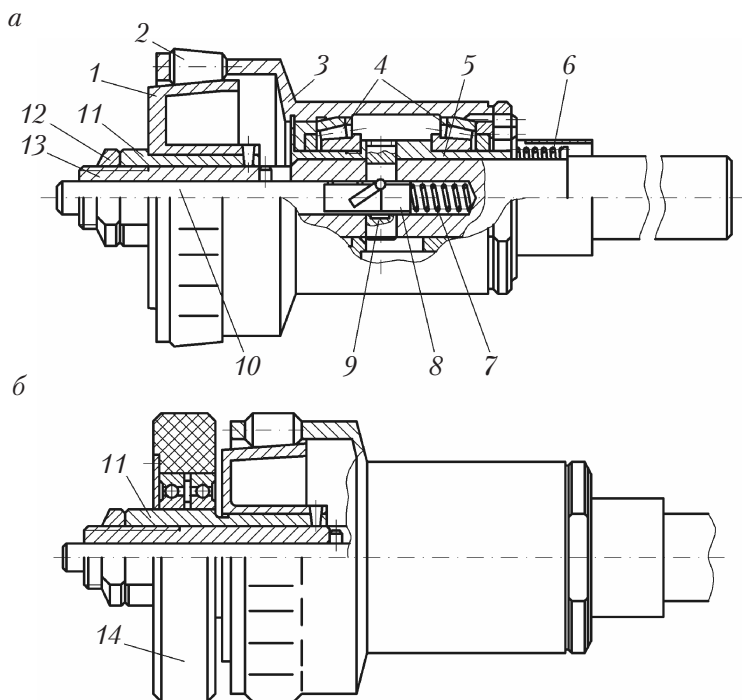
Многороликовое приспособление для обработки ППД отверстий в заготовках из чугуна
